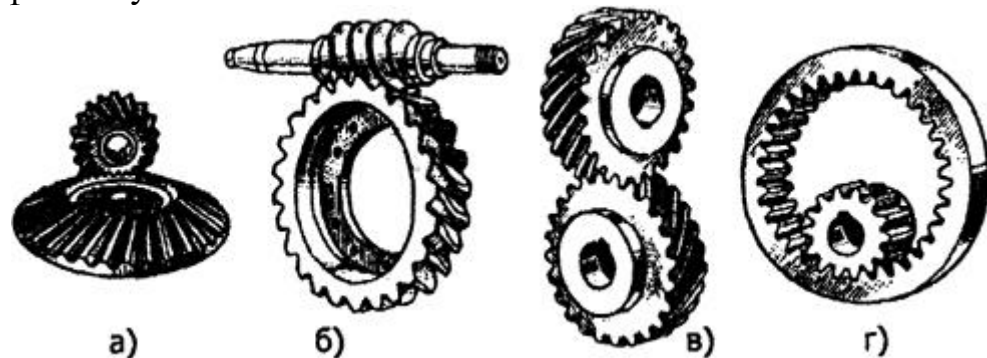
Зубчатые передачи: а - коническая, б - червячная, в - винтовая, г - цилиндрическая с внутренним зацеплением
